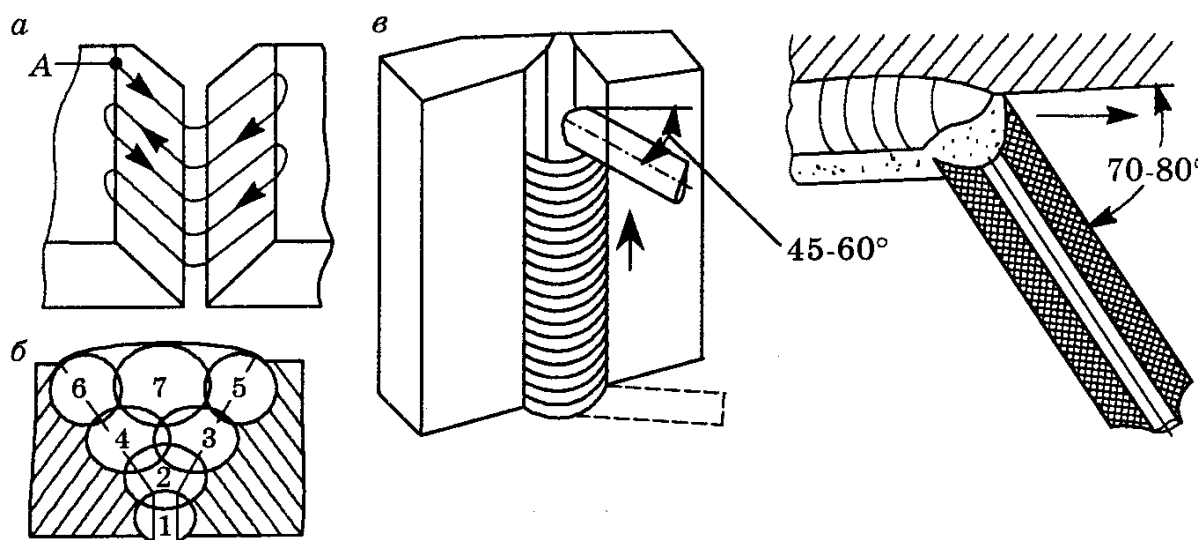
Положение и движения электрода при сварке однослойных швов
